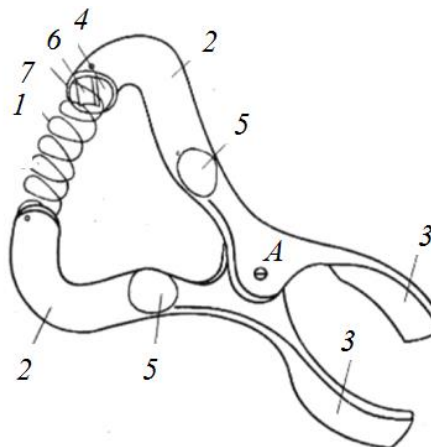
Устройство для ручного сбора ягод (А. с. 1395192)
